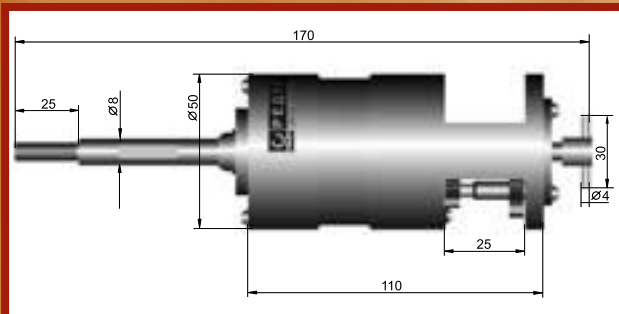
Габаритные размеры цилиндрико-планетарного редуктора
